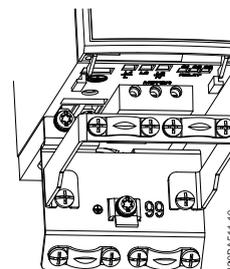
Conversor de frequência com placa de desacoplamento
